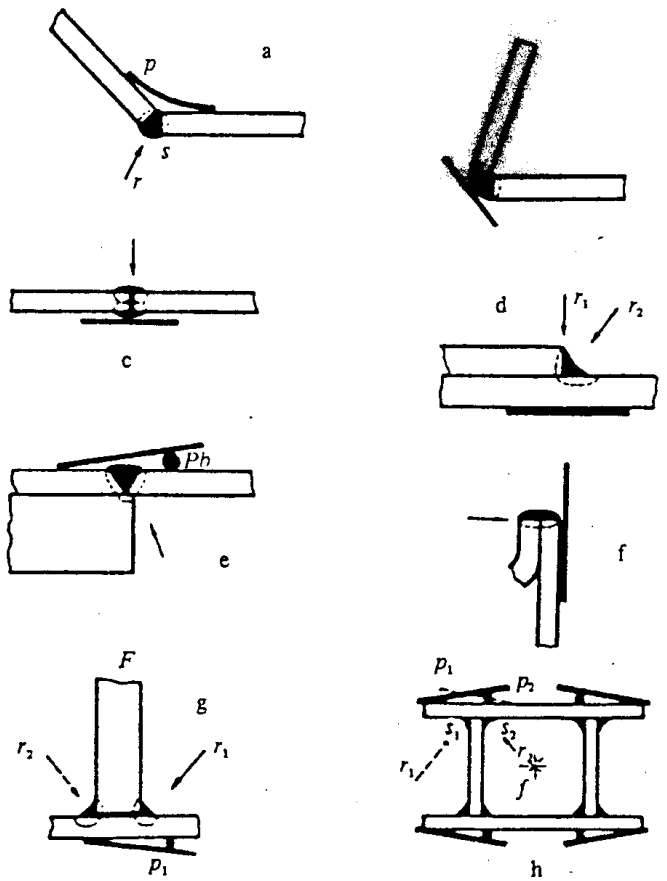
Radiografiado de soldaduras en ángulo.
